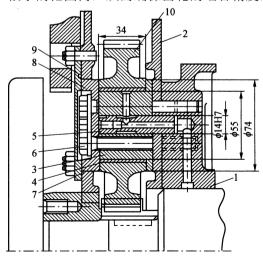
正时中间齿轮机构 1. 气缸体 2. 正时齿轮室 3. 轴承座 4. 轴承衬套 5. 芯轴 6. 轴承座固定螺栓 7. 0 形圈 8. 轴承压 盖 9. 压板 10. 正时中间齿轮
